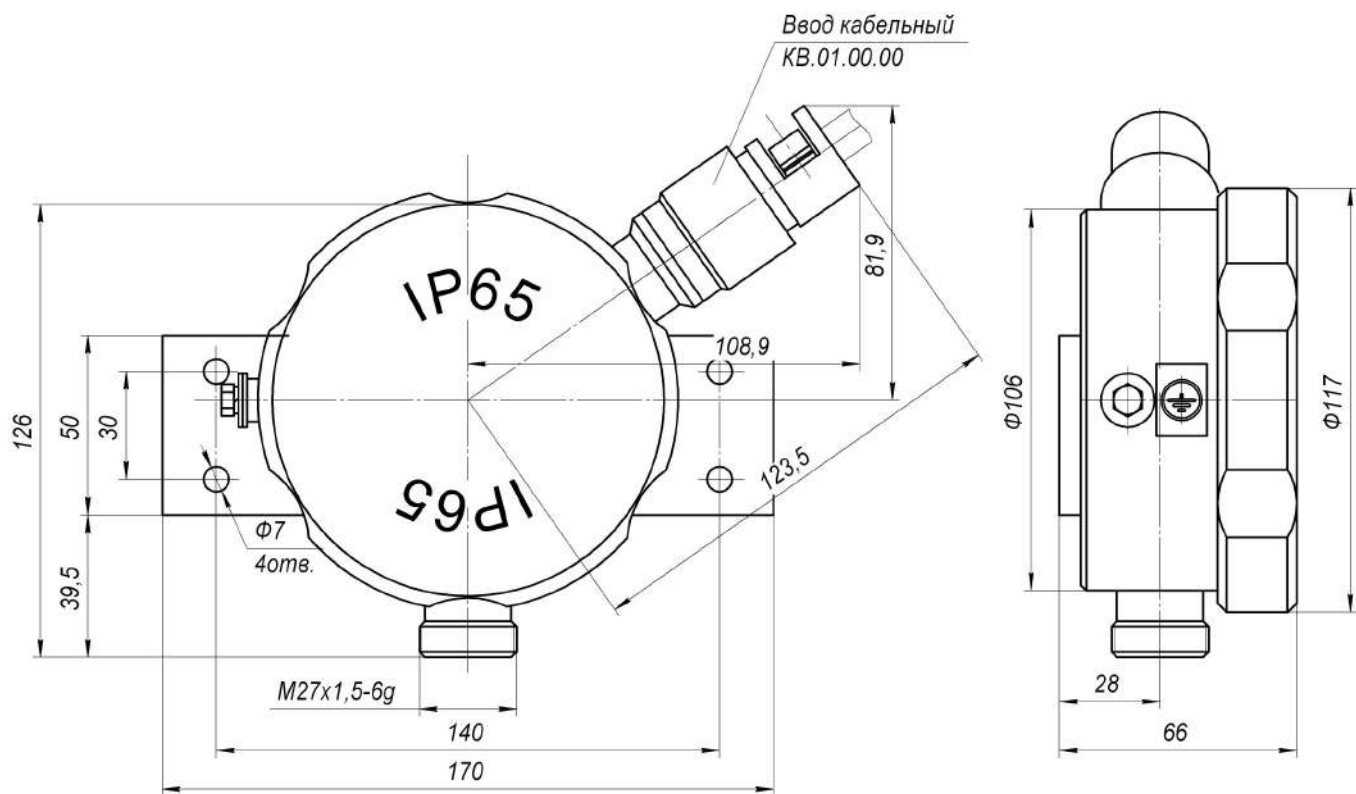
Корпус «Н» ПП из стали 12Х18Н10Т
